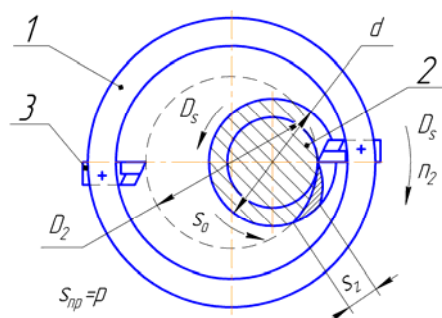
Схема вихревого нарезания резьбы: 1 – вихревая головка; 2 – нарезаемый ходовой винт; 3 – фасонный стержневой резец;  $D$  – диаметр головки;  $d$  – диаметр нарезаемого винта;  $s_0$  – круговая подача, мм/зуб;  $s_{np}$  – продольная подача, мм/об
